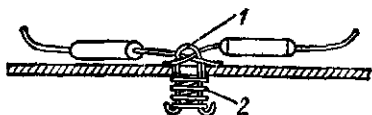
Монтажный лепесток и установка его на монтажную планку
